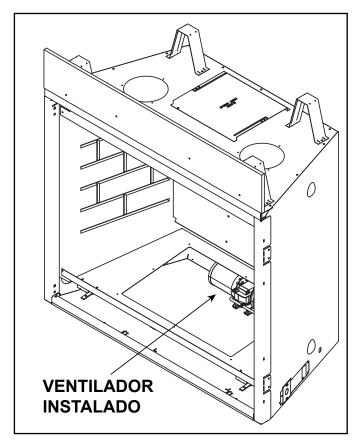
Ventilador instalado en la cavidad de la placa de la válvula
